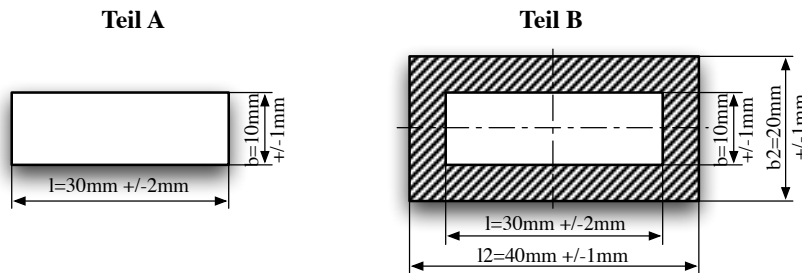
CAD Zeichnung mit Bemaßung.
